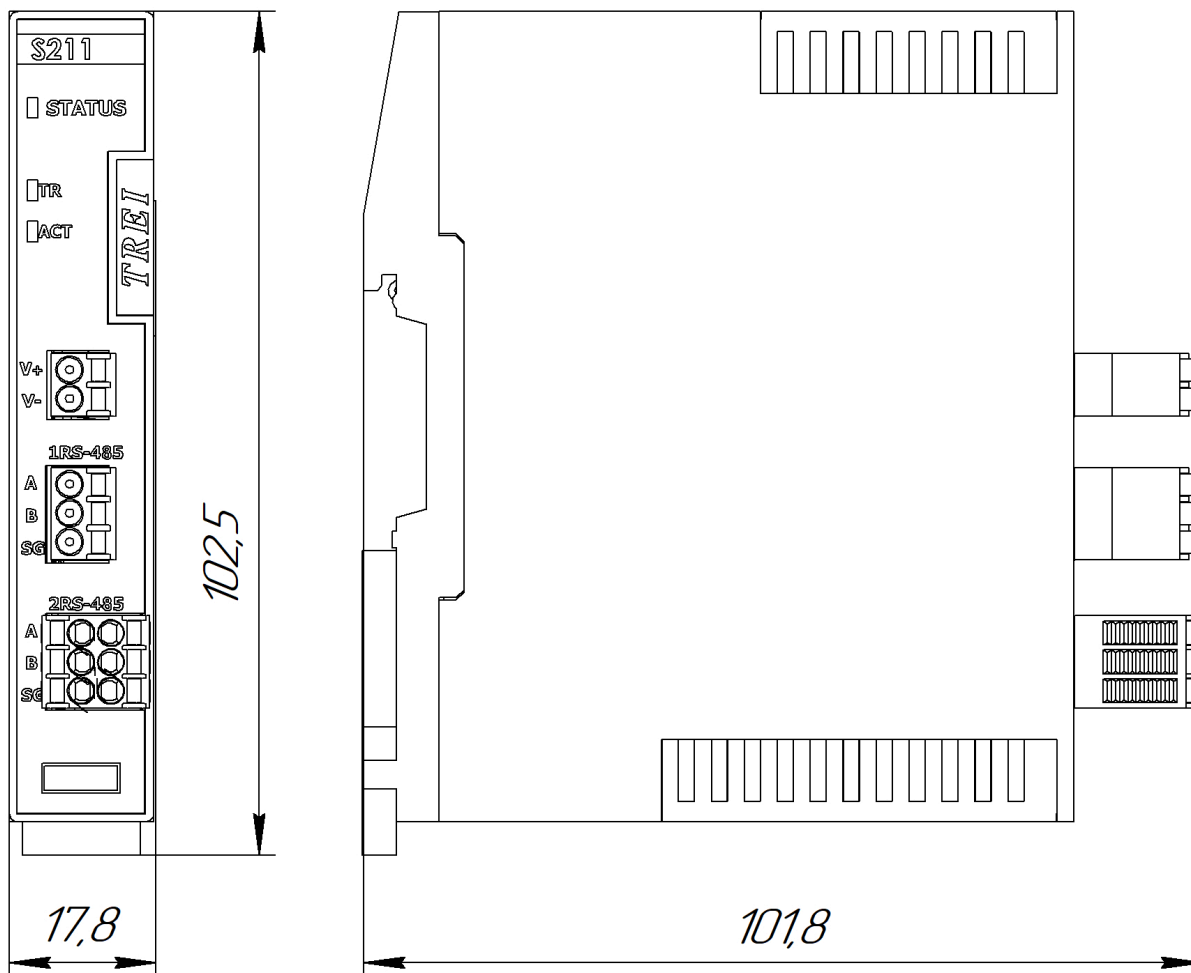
Чертеж общего вида S211 с указанием габаритных и присоединительных размеров
